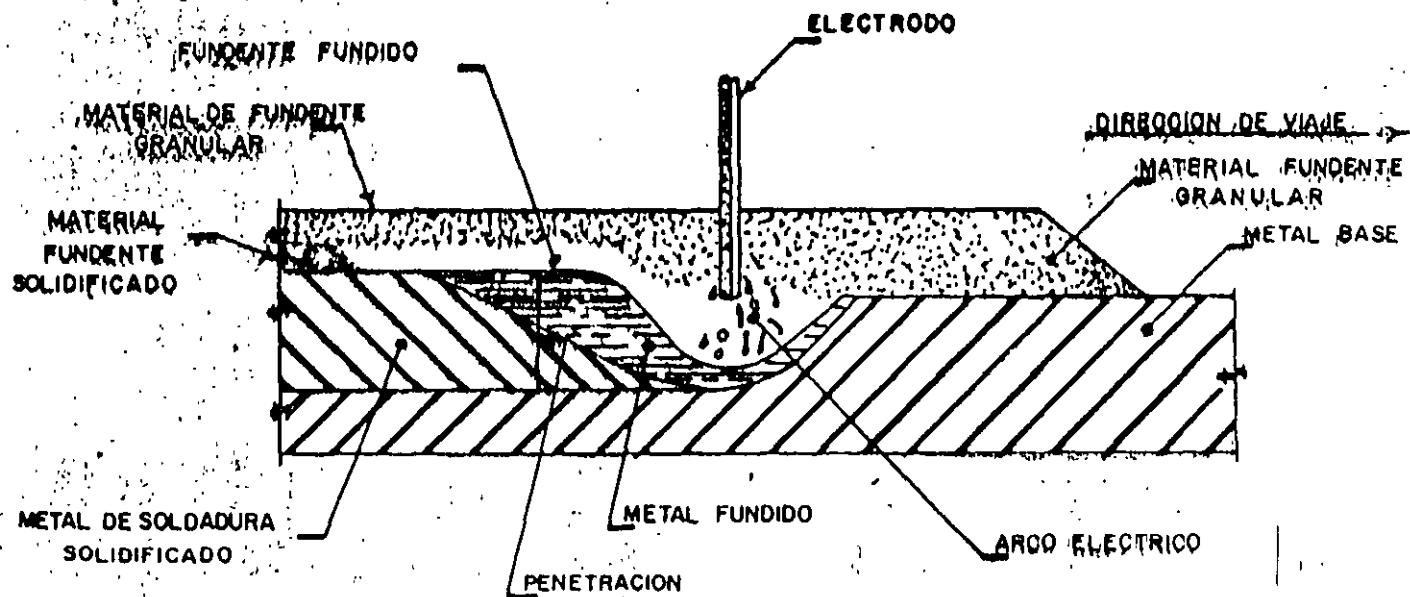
FIG. II- SOLDADURA DE ARCO CON PROTECCION
